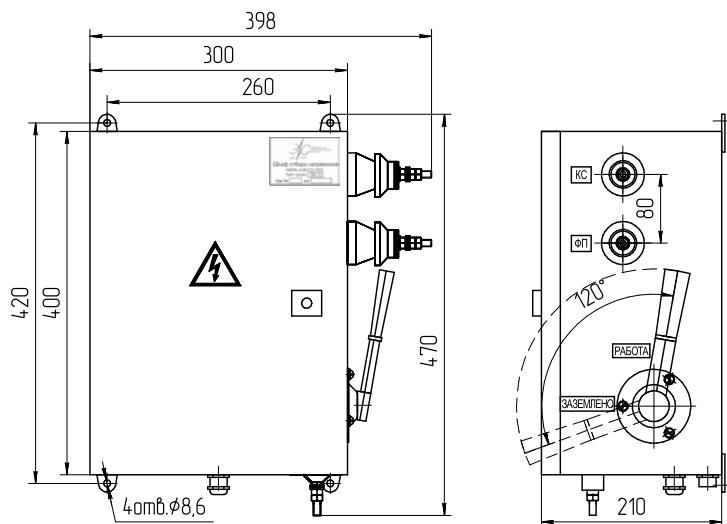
Габаритно-присоединительный чертеж ШОН-301С.
